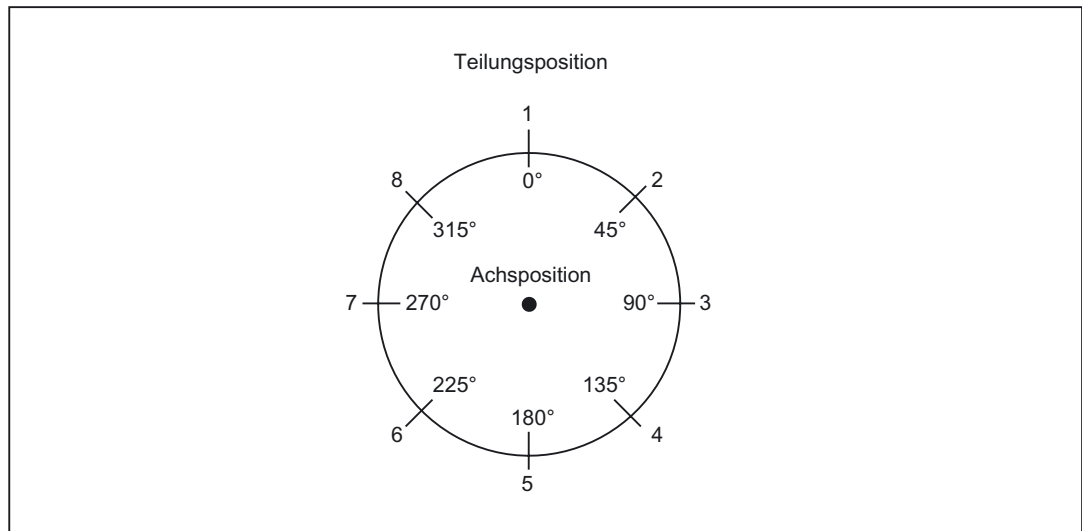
Beispiel: Werkzeug-Revolver mit 8 Plätzen
